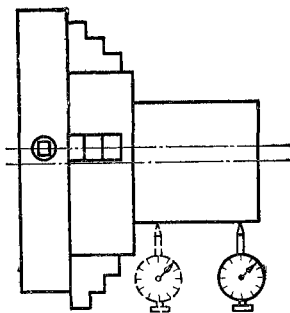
Установка эксцентриковой заготовки в четырехкулачковом патроне с выверкой по индикатору
